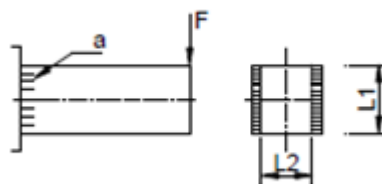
Esquema para cálculo de esfuerzos en el cordón de soldadura
